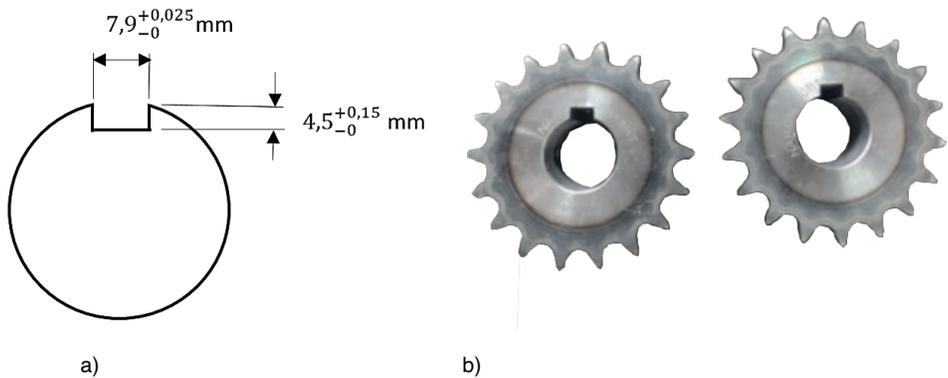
Dimensiones de chaveteros: a) dimensión de chavetero en los rodillos, b) piñones con chavetero
